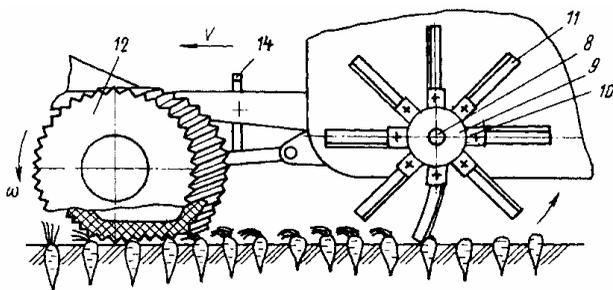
Катки и ротор очистителя (вид сбоку)
